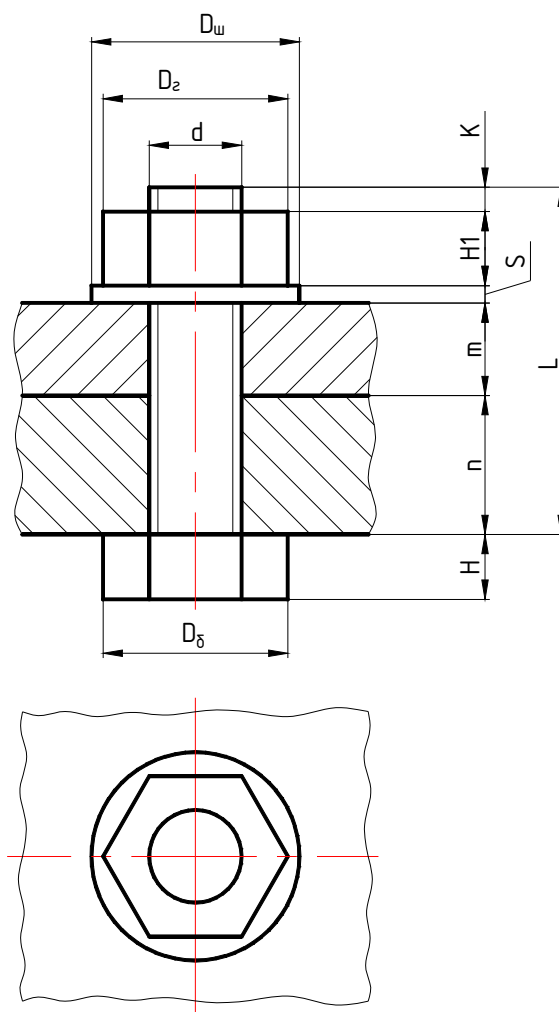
Чертеж болтового соединения с буквенными обозначениями
